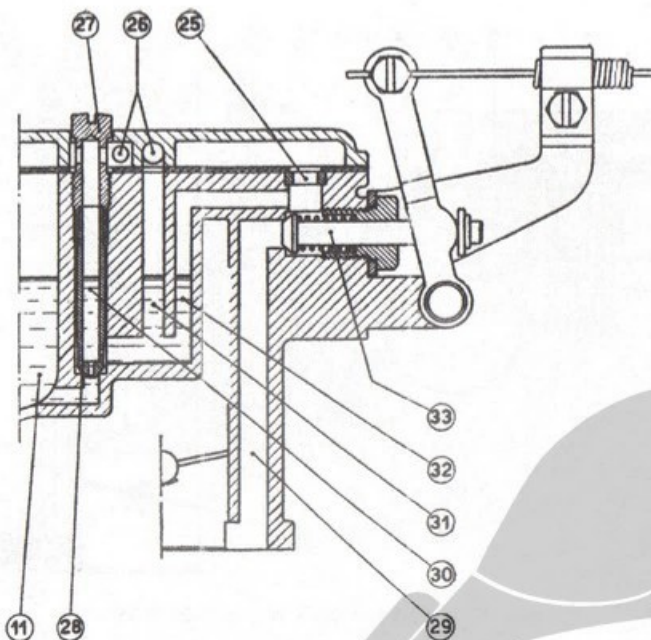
Dispositivo d'avviamento del carburatore «Weber» 22 DRS.
